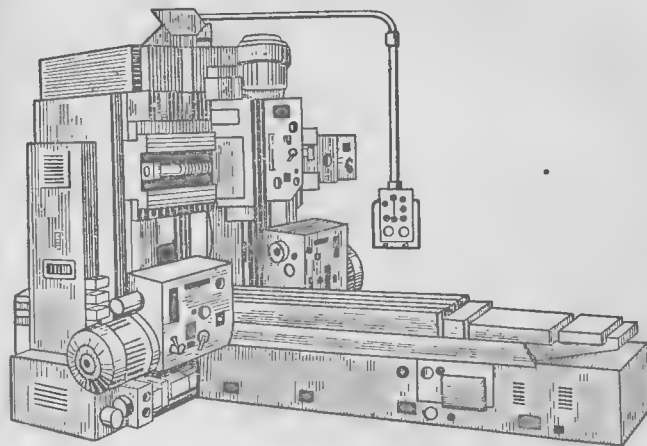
Двухстоечный продольно-фрезерный станок.
